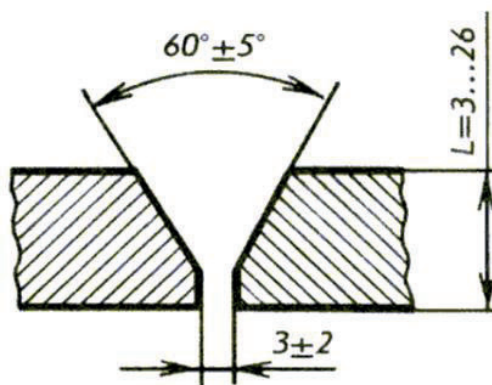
Підготовка кромки металу товщиною 3-26 мм до зварювання
